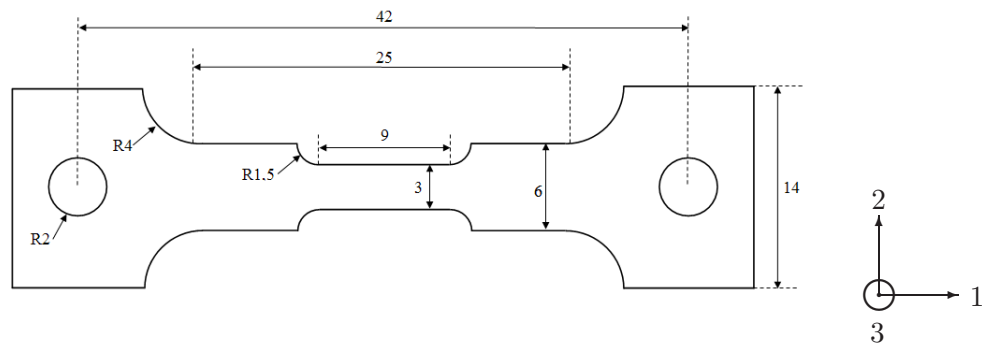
Géométrie de l'éprouvette, dimensions en mm
